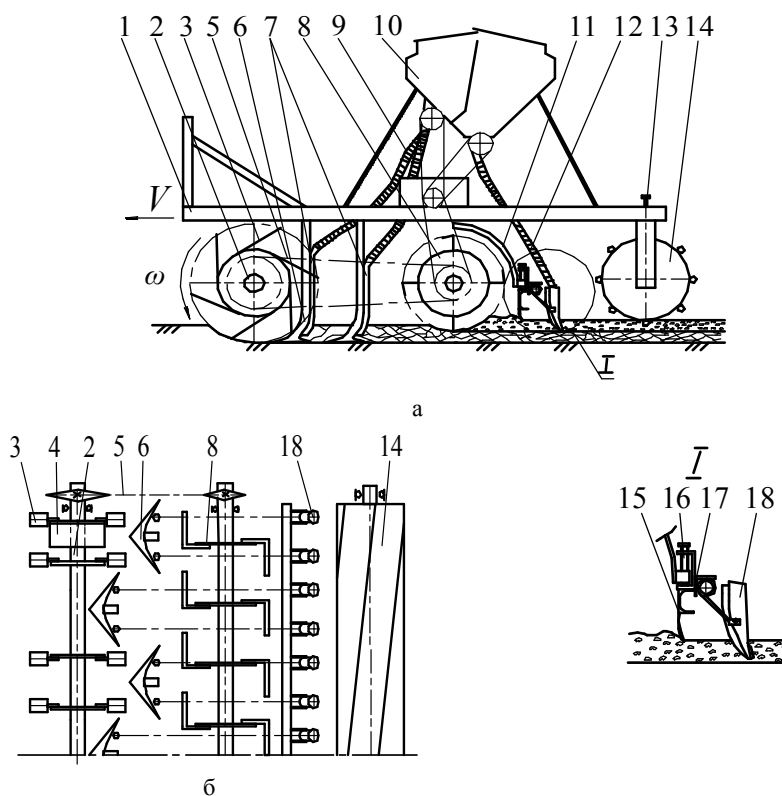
Почвообрабатывающе-посевной агрегат: а – вид сбоку; б – схема размещения рабочих органов: 1 – рама; 2 – ротор приводной; 3 – почвозацепы; 4 – опорные реборды; 5 – цепная передача; 6 – культиваторные лапы; 7 – туюководы; 8 – измельчающий ротор; 9 – коробка перемены передач; 10 – зернотуковый ящик; 11 – защитный кожух; 12 – семяпроводы; 13 – механизм регулировки глубины обработки; 14 – каток; 15 – выравниватель; 16 – механизм регулировки глубины посева; 17 – брус сошников; 18 – сошники
